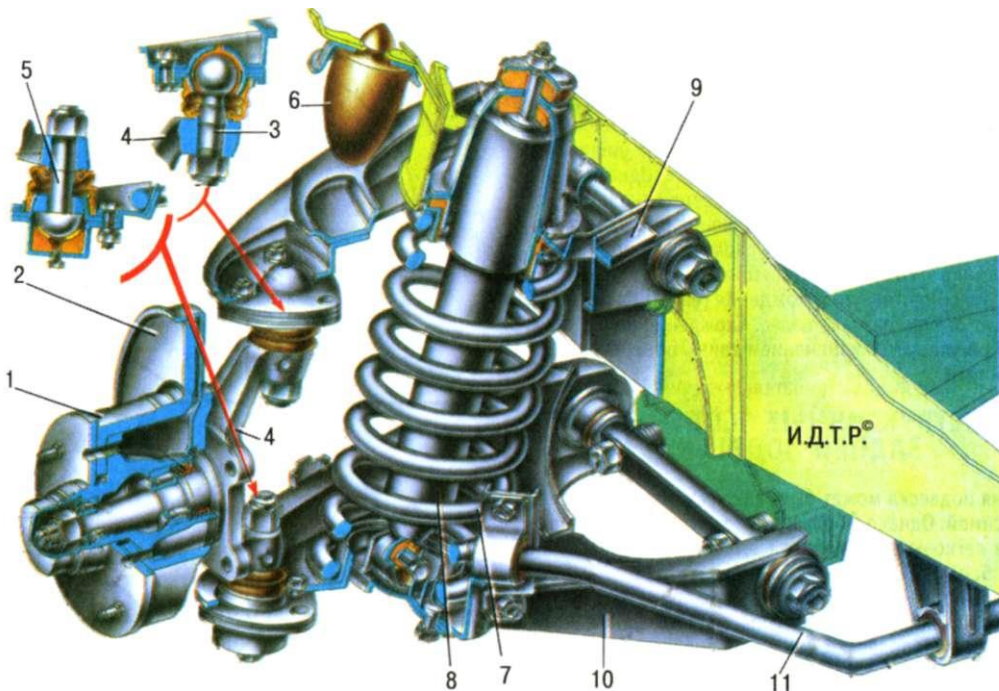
Передняя подвеска: 1 - ступица колеса; 2 - тормозной диск; 3 - шаровой палец верхней опоры; 4 - поворотный кулак; 5 - шаровой палец нижней опоры; 6 - буфер хода сжатия; 7 - пружина подвески; 8 - амортизатор; 9 - верхний рычаг подвески; 10 - нижний рычаг подвески; 11 - штанга стабилизатора
